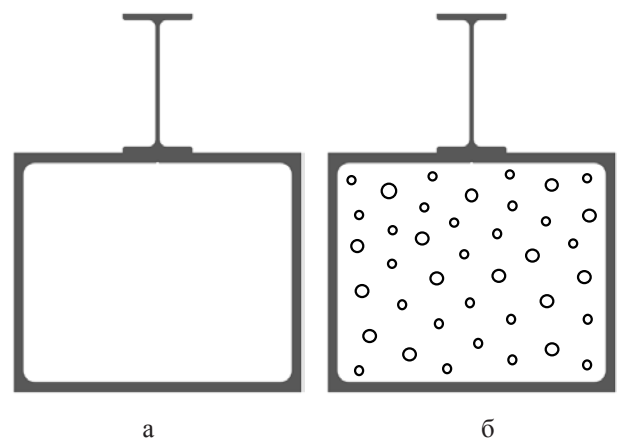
Переріз замкненої конструкції хребтової балки напіввагона: а) без наповнювача; б) з наповнювачем
